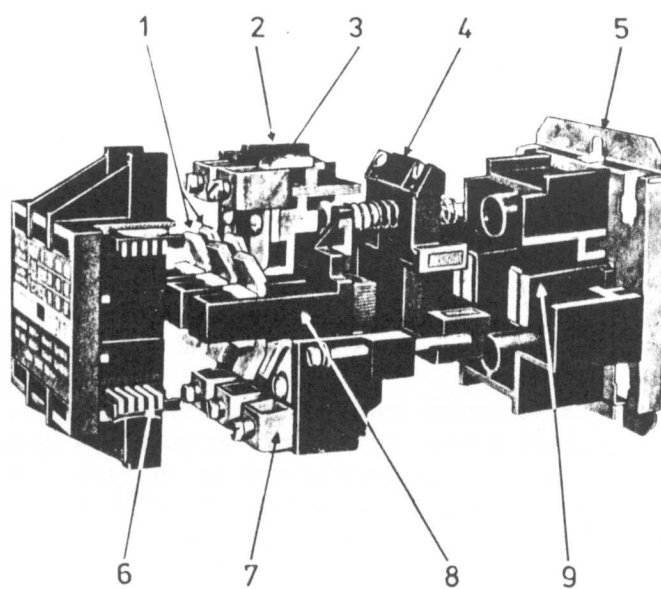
Estructura del contactor AGUT tipo CK: 1.Contactos fijos y móviles de diseño especial, con plaquitas de contacto de plata-óxido de cadmio, soldadas, 2.soporte de contactos fijos moldeado con material aislante, altamente resistente a las líneas de fuga, 3.Bobina completamente encapsulado para su completa protección mecánica y atmosférica, 4.Bornes para embornar pletinas y terminales, 5.Soporte de base metálico con alejamiento en cada esquina para bloque de dos contactos auxiliares, 6.Extintores de arco De-ión, alojados en tapa frontal moldeada con material aislante altamente resistente al arco, 7.Bornes tipos mordaza, de gran capacidad y fácilmente accesibles, 8.Soporte portacontactos móviles y portamertillo moldeado con material aislante altamente resistente al arco, 9.Circuito magnético en forma de U y con entrehierro fijo.
